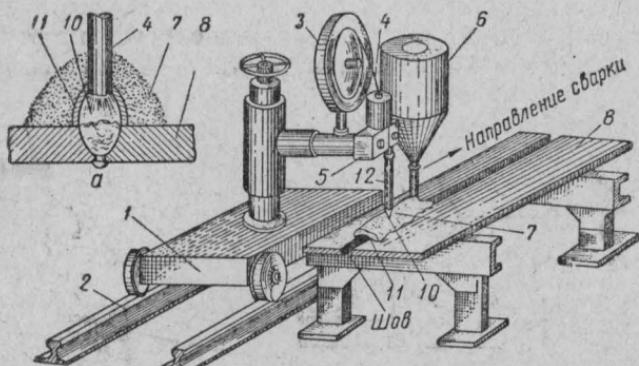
Схема установки для автоматической сварки под флюсом:
